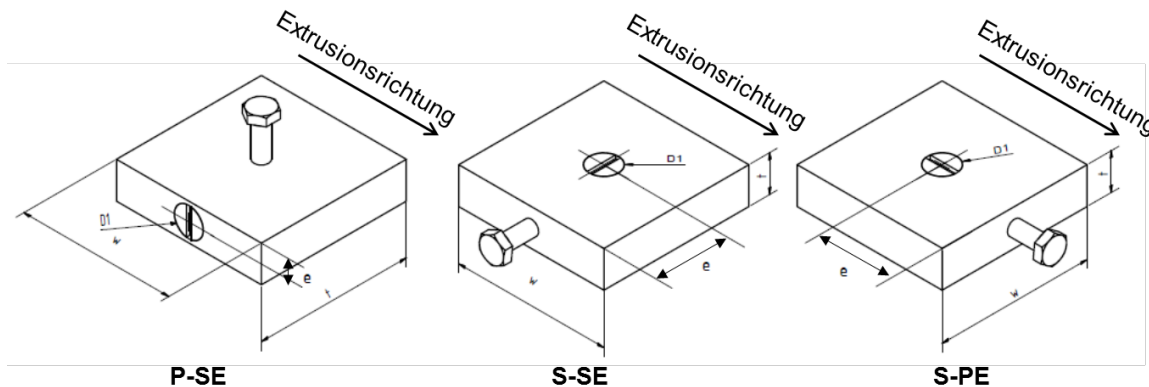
Konstruktiv relevante Einschraubrichtungen der QGB-Steckschraubverbindung in plattenförmigen Halbzeugen aus WPC
